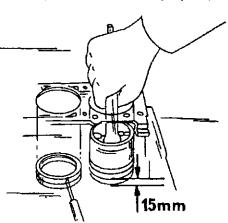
Измерение стыкового зазора поршневых колец в нижней части рабочей гильзы цилиндра.
